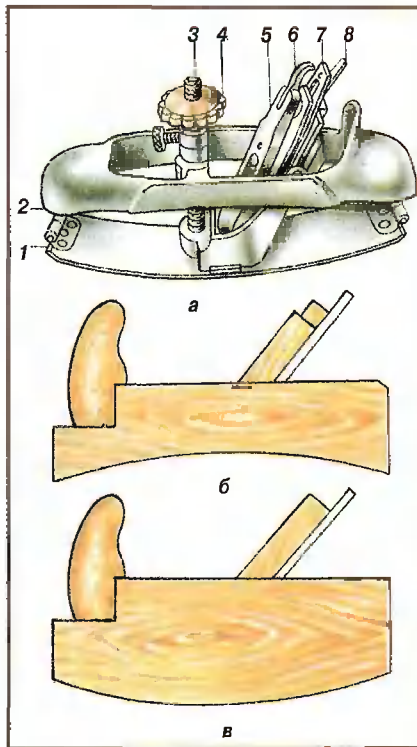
Рубанки-горбачи: а — универсальный металлический рубанок-горбач (1 — подошва; 2 — колодка; 3 — винт регулировки кривизны подошвы; 4 — гайка-регулятор кривизны подошвы; 5 — прижим; 6 — защелка; 7 — нож; 8 — вилка крепления ножа); б, в — деревянные горбачи для строгания выпуклой и вогнутой поверхностей соответственно.
